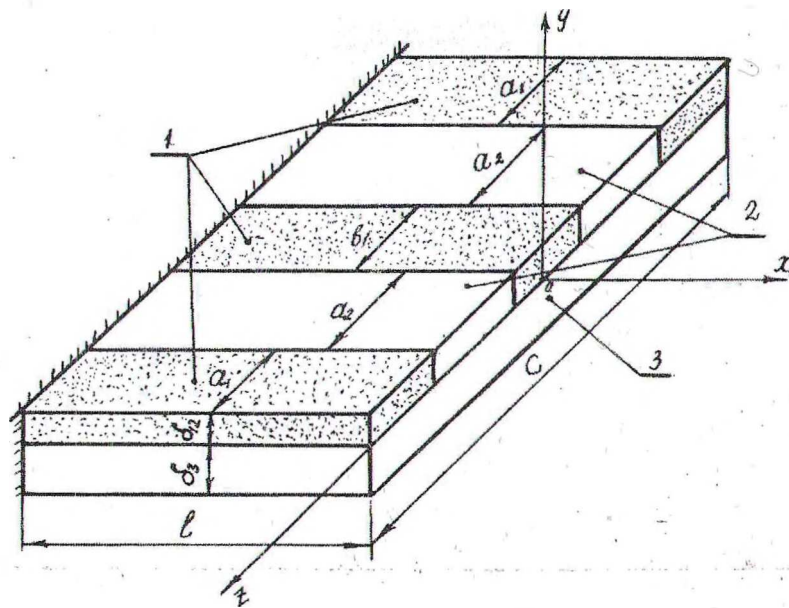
Схема заготовки для композиционного ножа: 1 – композиционный порошковый износостойкий материал; 2 – износостойкий твердый сплав; 3 – корпус ножа
